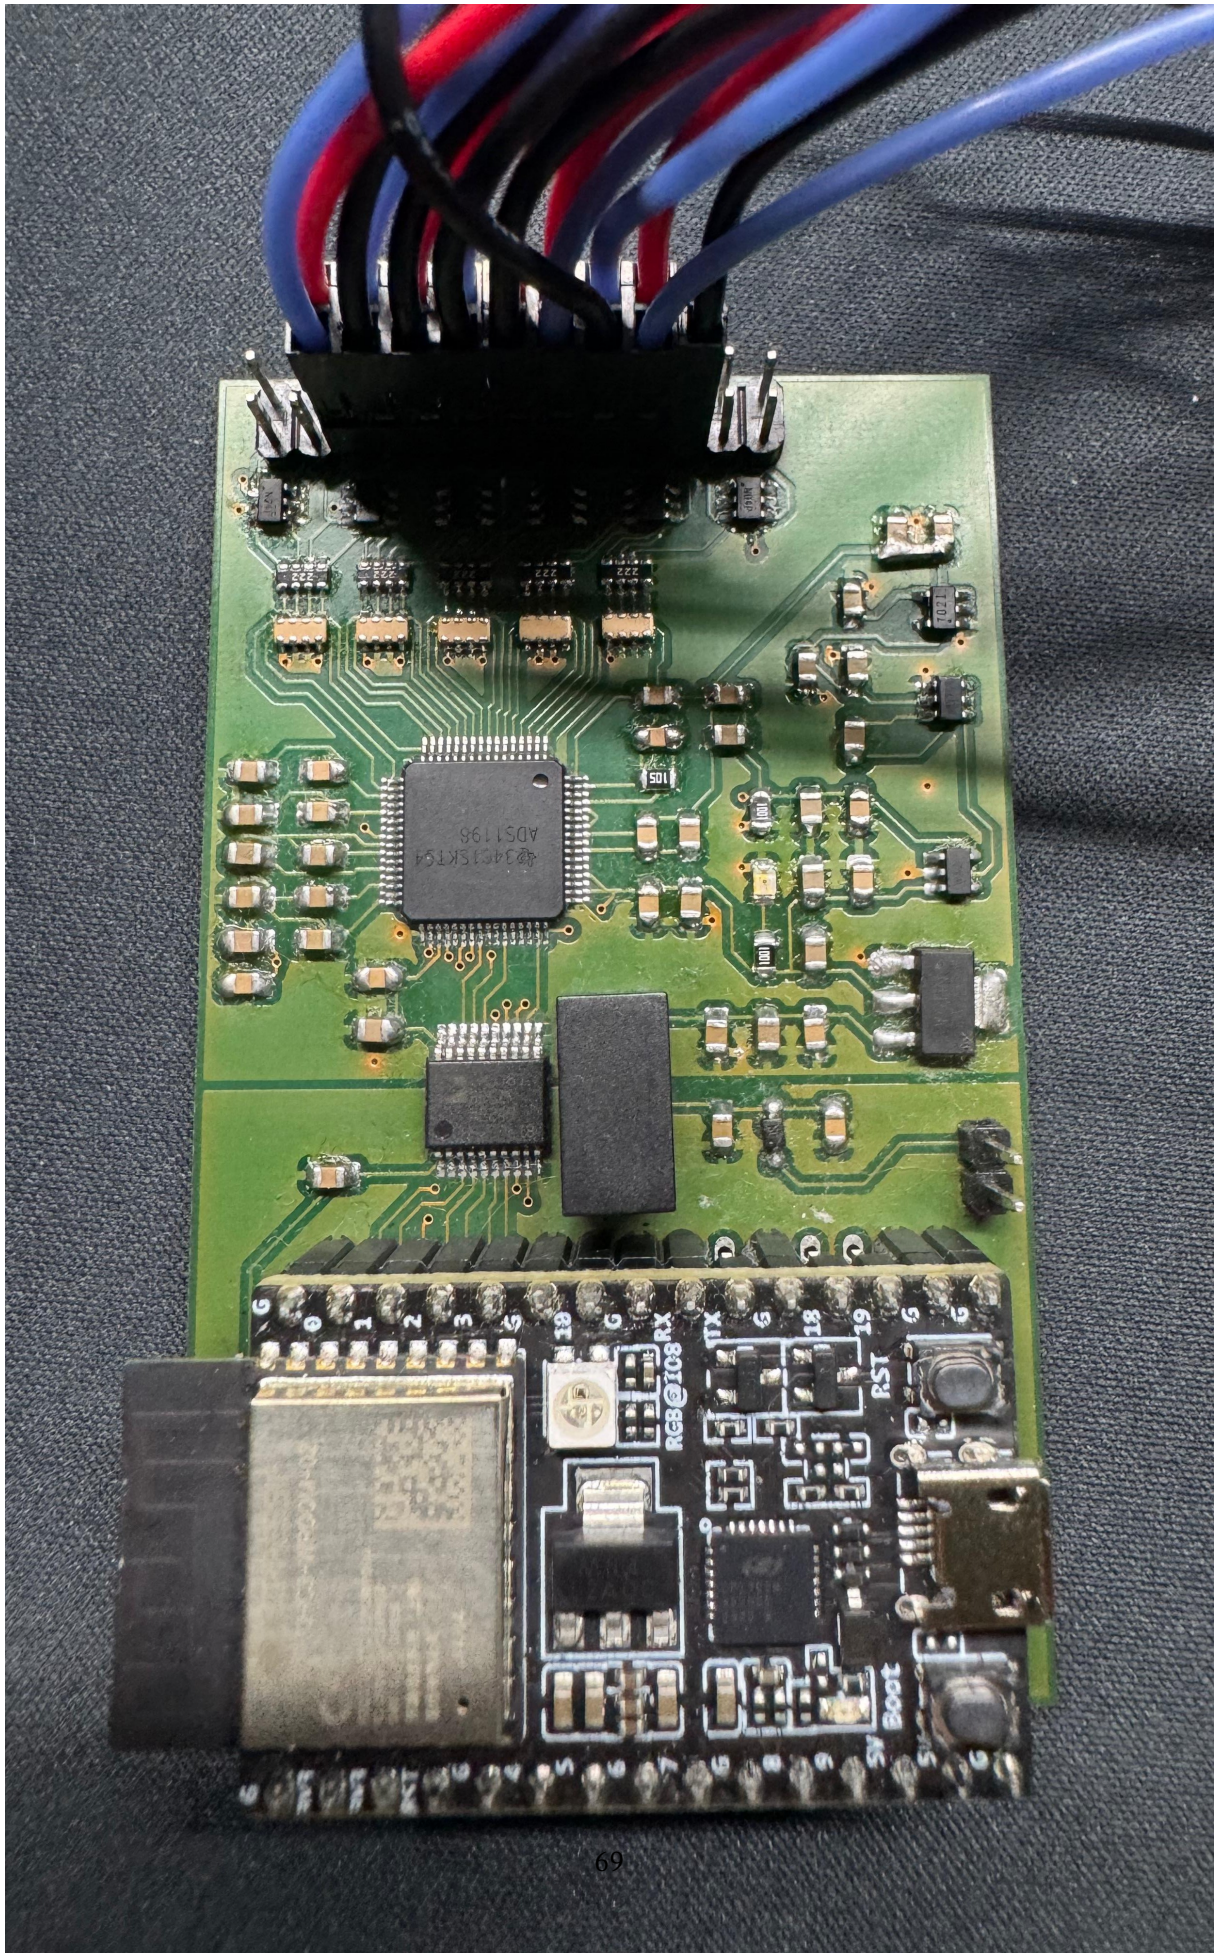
Vista frontal de la PCB ya soldada
